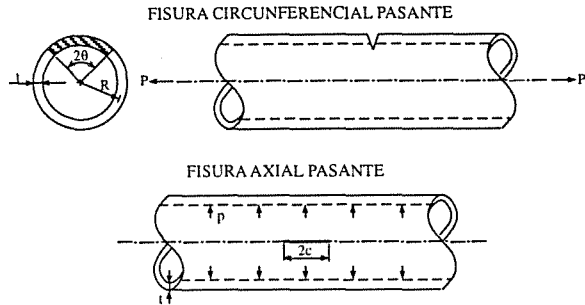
Geometría y sistema de cargas de las fisuras postuladas
